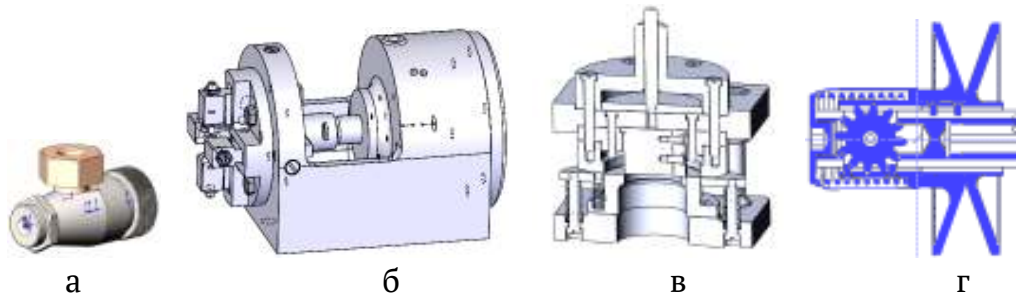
Форсунка (а), пристосування для хрестового обтиску прутка (б), штамп для виготовлення пластин (в), клинопасовий варіатор (г)
